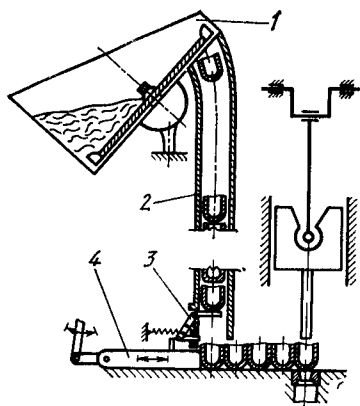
Автоматизированная загрузка прессы штучными заготовками
